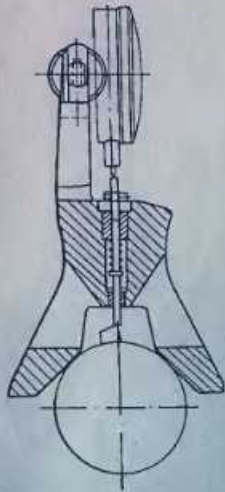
Индикаторное приспособление для установки реза в борштанге
